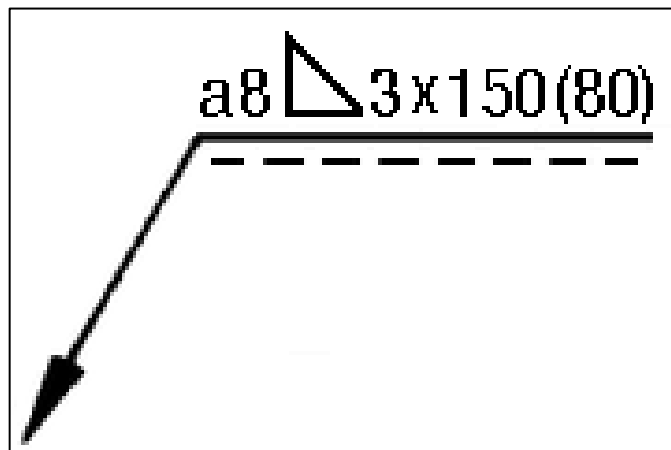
Dimensiones por indicar en un plano de soldadura
